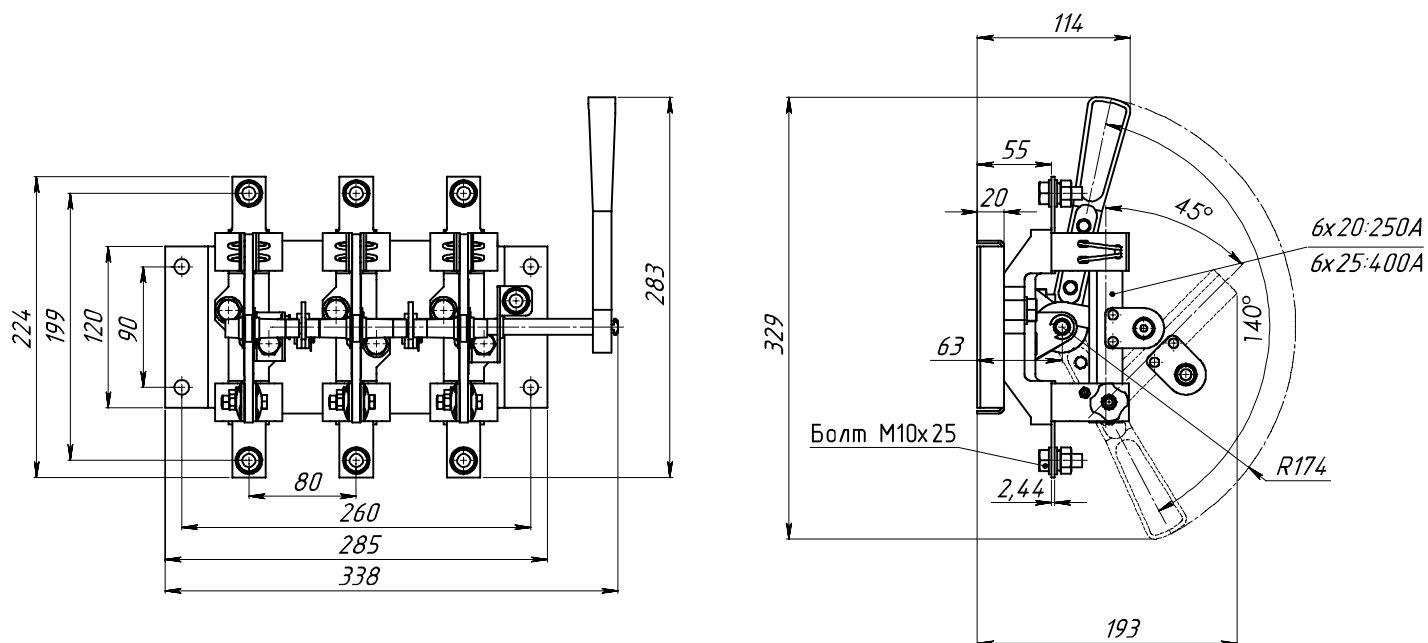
Разъединитель PE19 трехполюсный с боковой рукояткой, переднего присоединения шин
